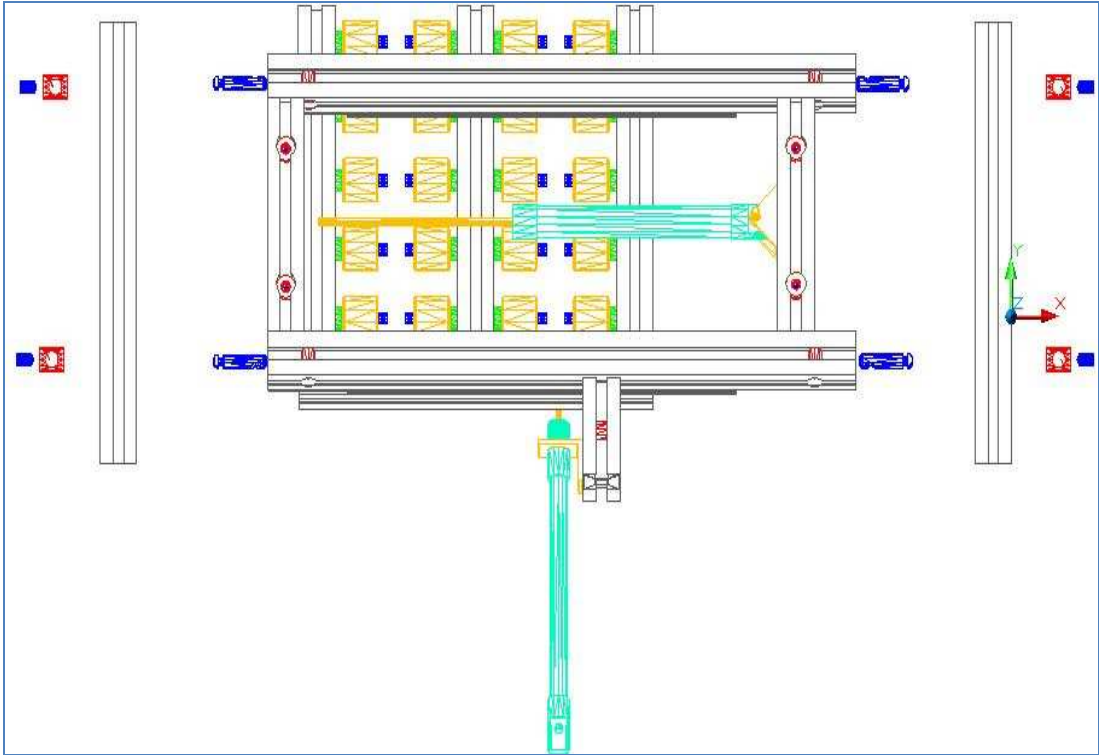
Vista Inferior estación de Almacenaje Eje X.
